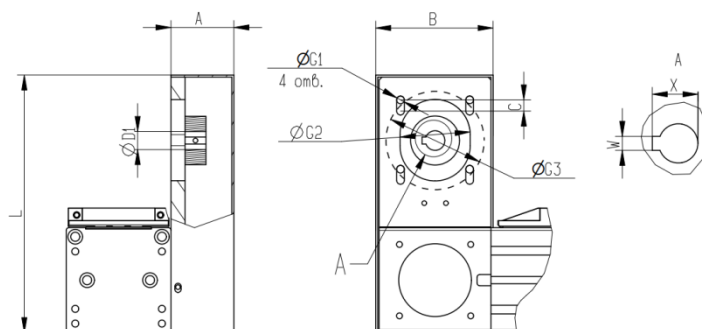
Набор для параллельной установки редуктора PR-MCR-112.
